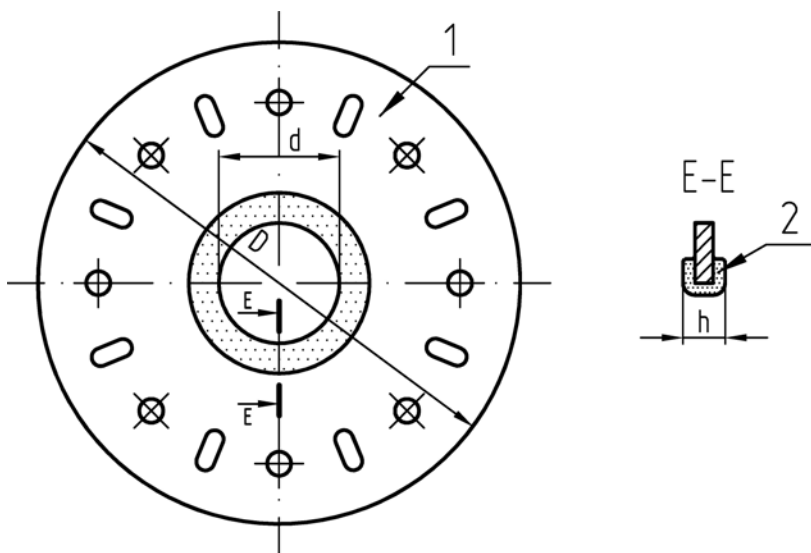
Конструкция алмазного диска с внутренней режущей кромкой:
